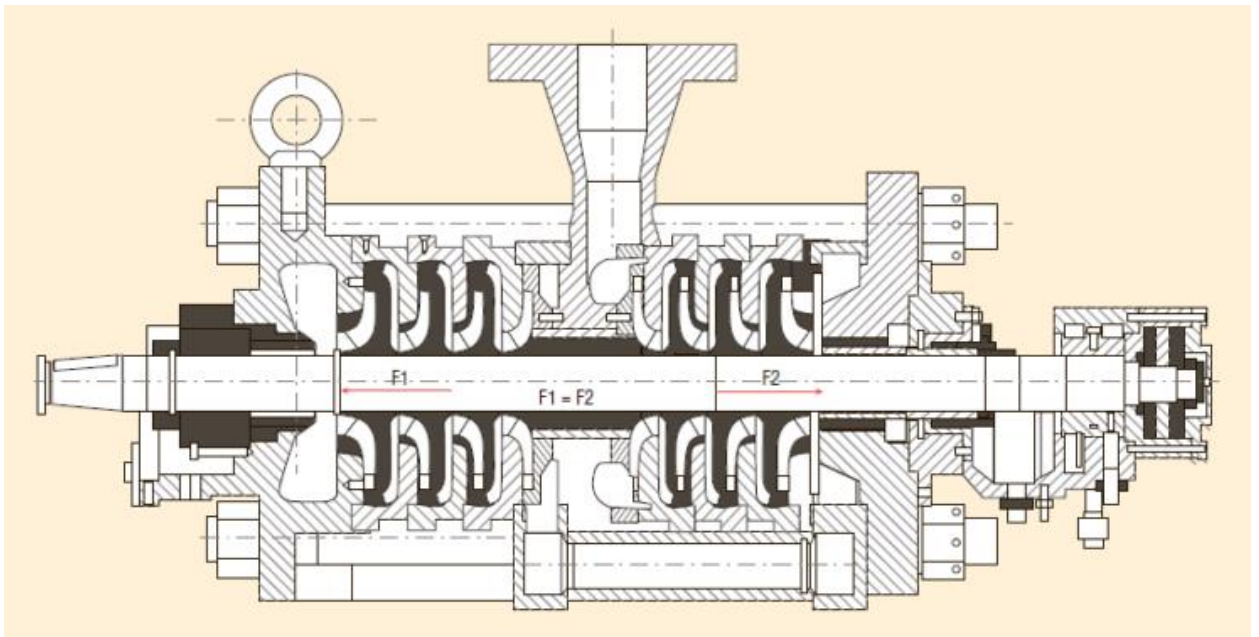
Насос ЦНС с оппозитным расположением рабочих колес
